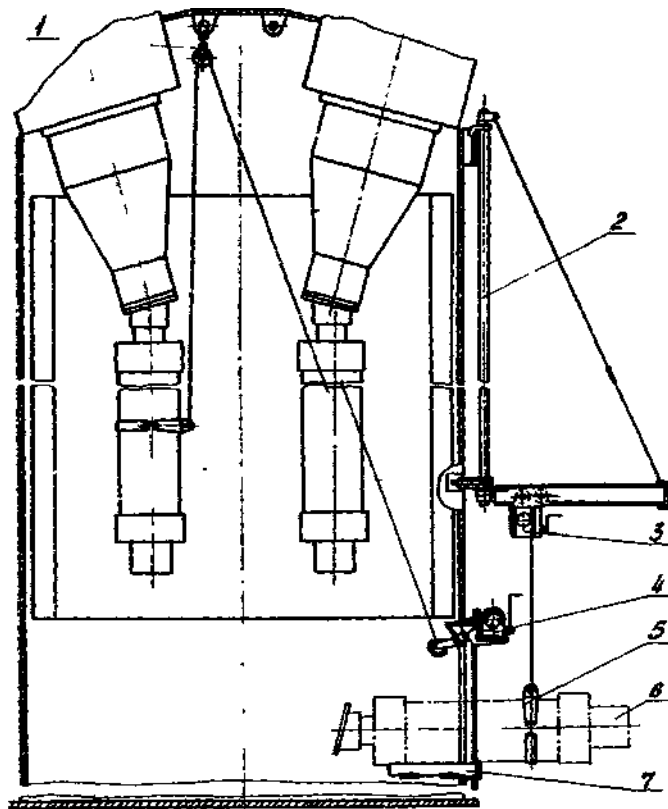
Установка приспособления для спуска и подъема камер масляного выключателя:
